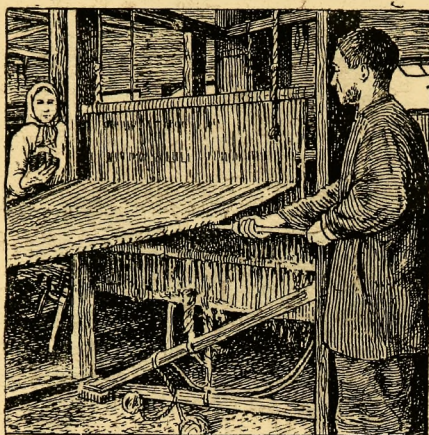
Ткацкий станок для выработки веревочных половиков. Вид со стороны ткача.
